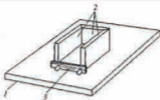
Модель крупного сушаря: 1 — гипсовая плита; 2 — гипсовые пластины; 3 — деревянная планка.
